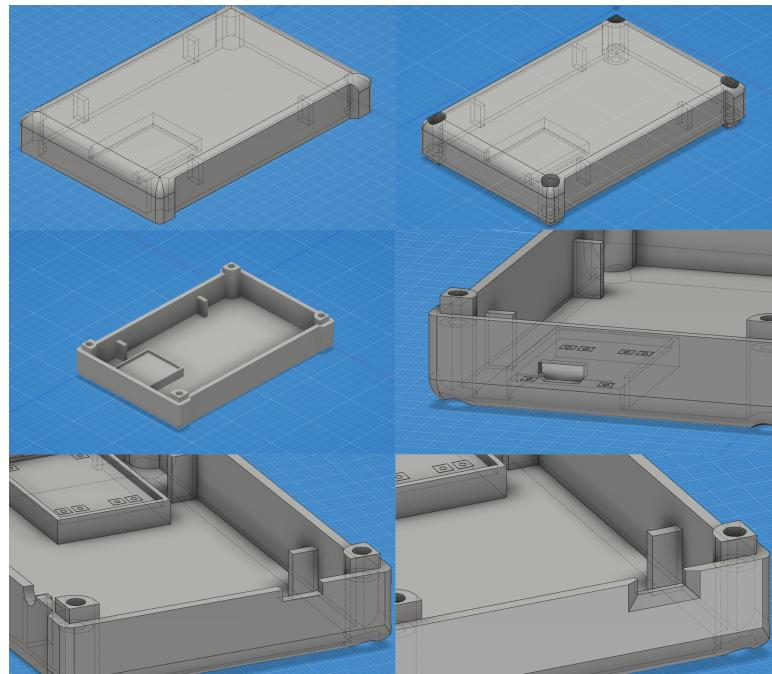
Proceso del diseño del molde inferior parte 2
